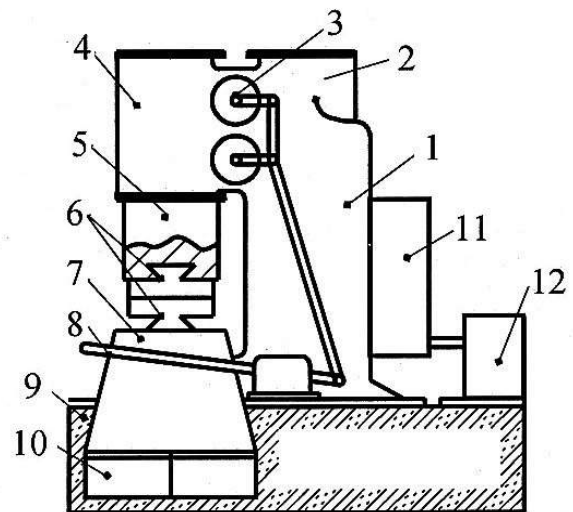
Загальний вигляд пневматичного молота: 1 – станина; 2 – компресорний циліндр; 3 – повітророзподільний пристрій; 4 – робочий циліндр; 5 – шток-поршень; 6 – бойки; 7 – шабот; 8 – педаль керування; 9 – фундамент; 10 – дубові бруси; 11 – редуктор; 12 – електродвигун
